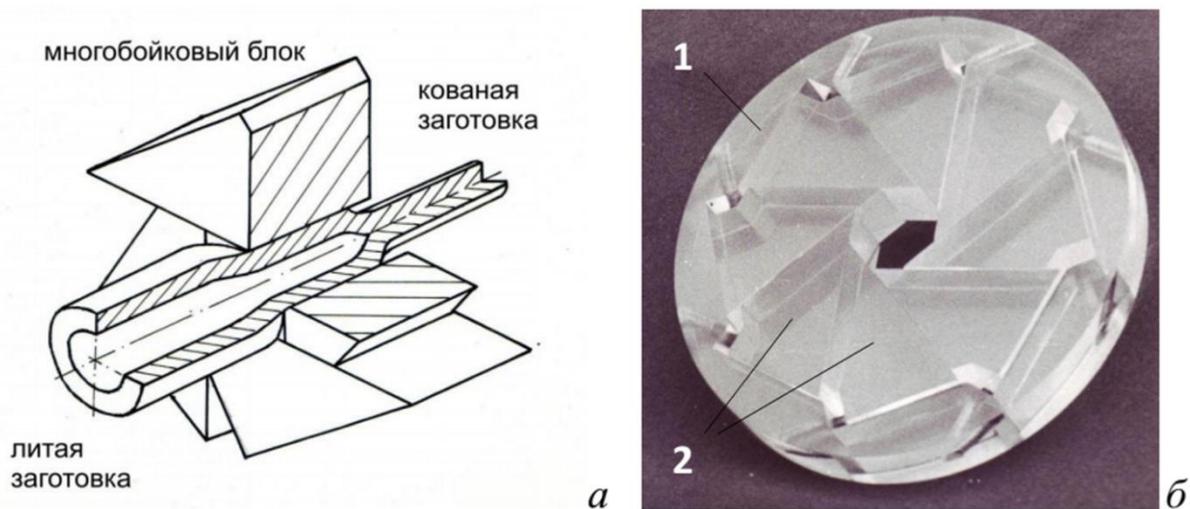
Схемаковки-протяжки (а) и 8-бойковый лабораторный блок (б): 1 – обойма; 2 – бойки
